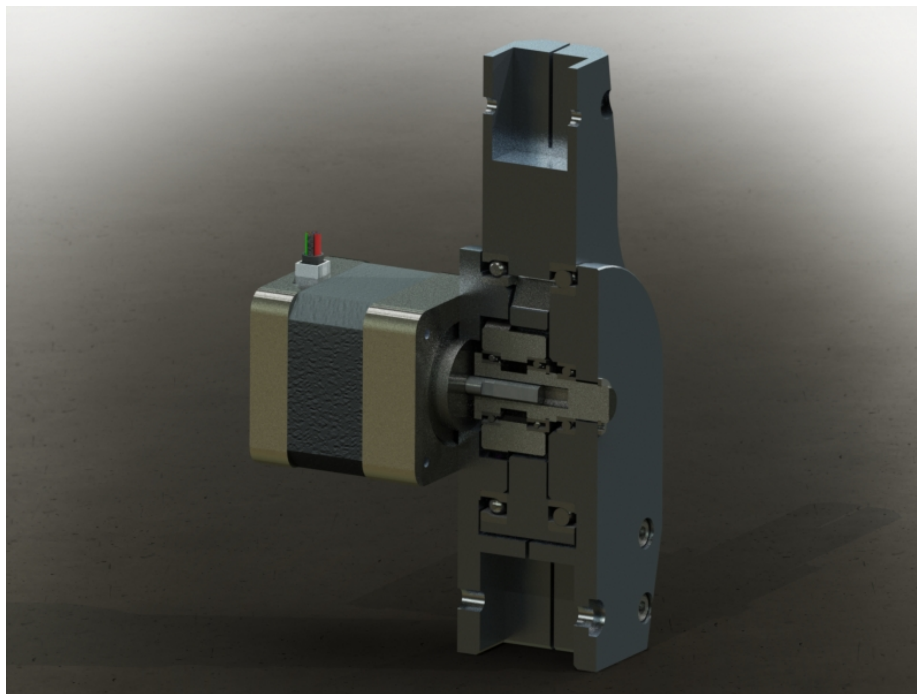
Конструкція поворотного вузла, що включає циклоїдальний редуктор
